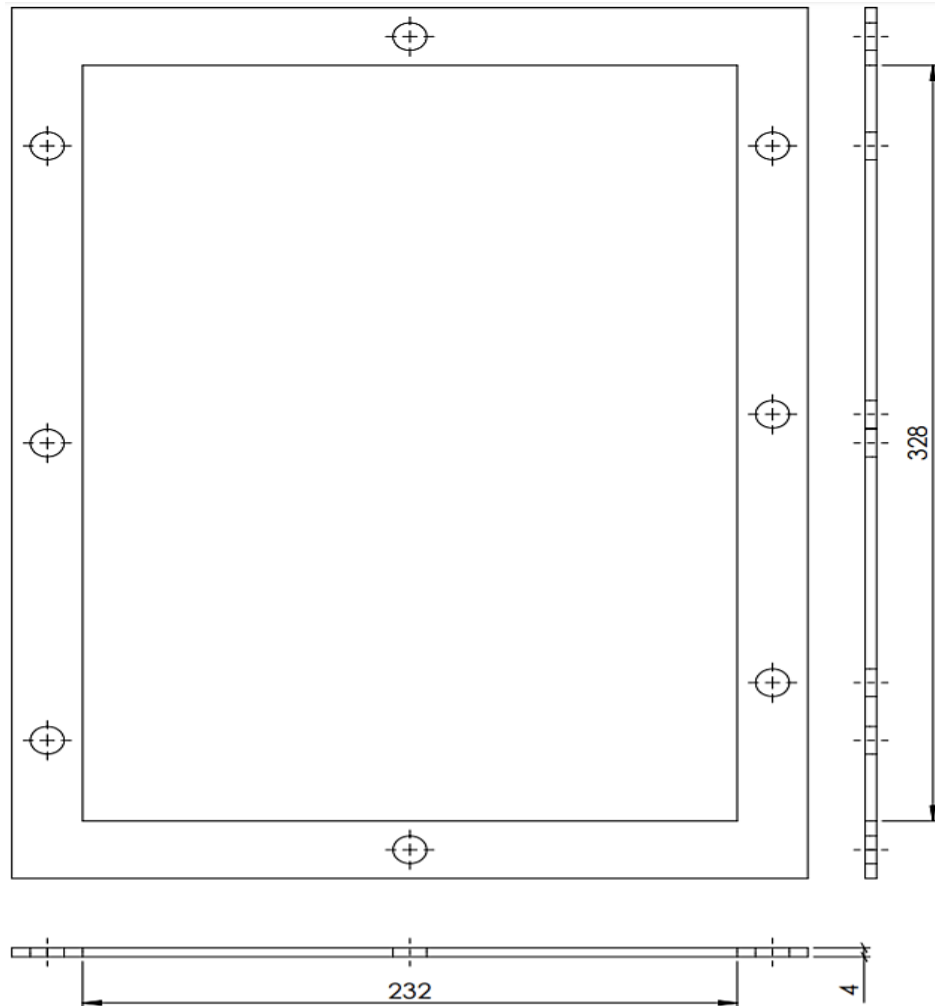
8 Diseño del molde (Dimensiones en mm)
